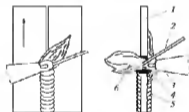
Схема сварки сквозным втягом:
